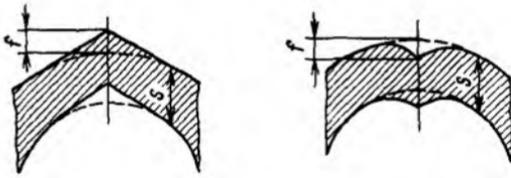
Увод (угловатость) кромок в сварных швах
